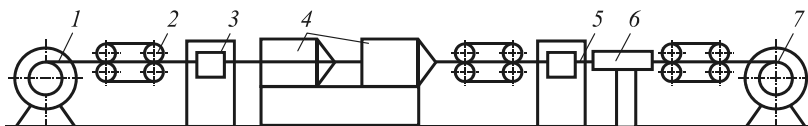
Схема линии сборки рукавов на гибких дорнах:
